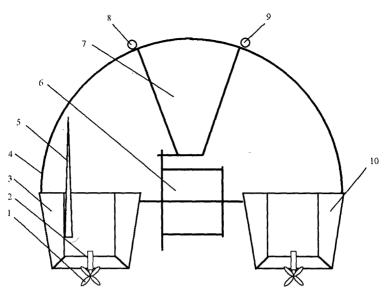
Вид со стороны кормы: 1 — винт; 2 — кожух вала винта; 3 — левый корпус катера; 4 — вертикальная стяжка; 5 — антенна; 6 — барабан прикормки; 7 — бункер; 8 — светодиод индикации работы приемника; 9 — светодиод индикации вращения барабана; 10 — правый корпус катера
